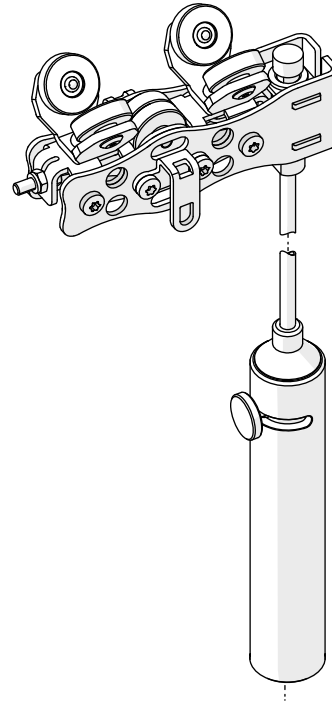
Abgeschlossener Umbau zu OFFICE Zugwagen mit Rastbremse
